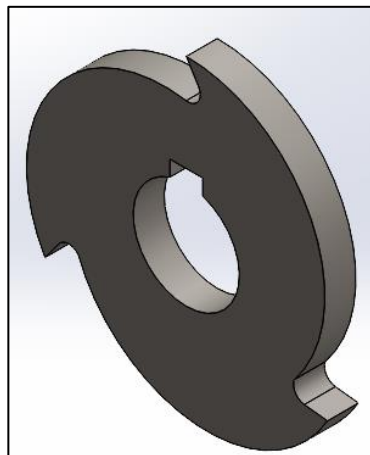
Vista isométrica de la cuchilla en SolidWorks
